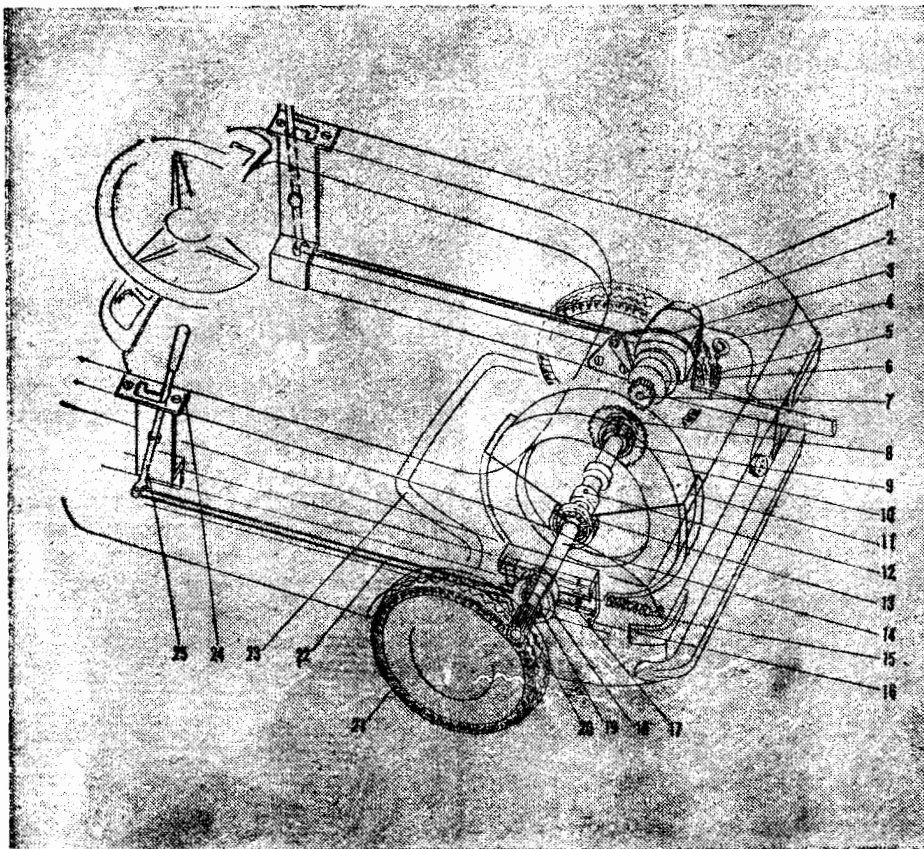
Общее расположение маховичного двигателя в кузове и механизмы управления: 1 — кузов, 2 — разгонный электродвигатель, 3 — рычажная подвеска, 4 — кожух, 5 — оттяжная пружина рукоятки включения, 6 — шариковая муфта электродвигателя, 7 — ведущая шестерня, 8 — ведомая шестерня маховика, 9 — муфта обгона, 10 — маховик, 11 — кожух маховика, 12 — муфта вала, 13 — подшипник кожуха, 14 — вал, 15 — оттяжная пружина вала, 16 — направляющие салазки, 17 — ползун, 18 — подшипник, 19 — обойма тяги переключателя второй передачи, 20 — фрикцион, 21 — ведущее колесо, 22 — тяга переключателя второй передачи, 23 — фигурная ось колес, 24 — фиксатор переключателя, 25 — рычаг (по правому) борту кузова — идентичный механизм включения первой передачи).
